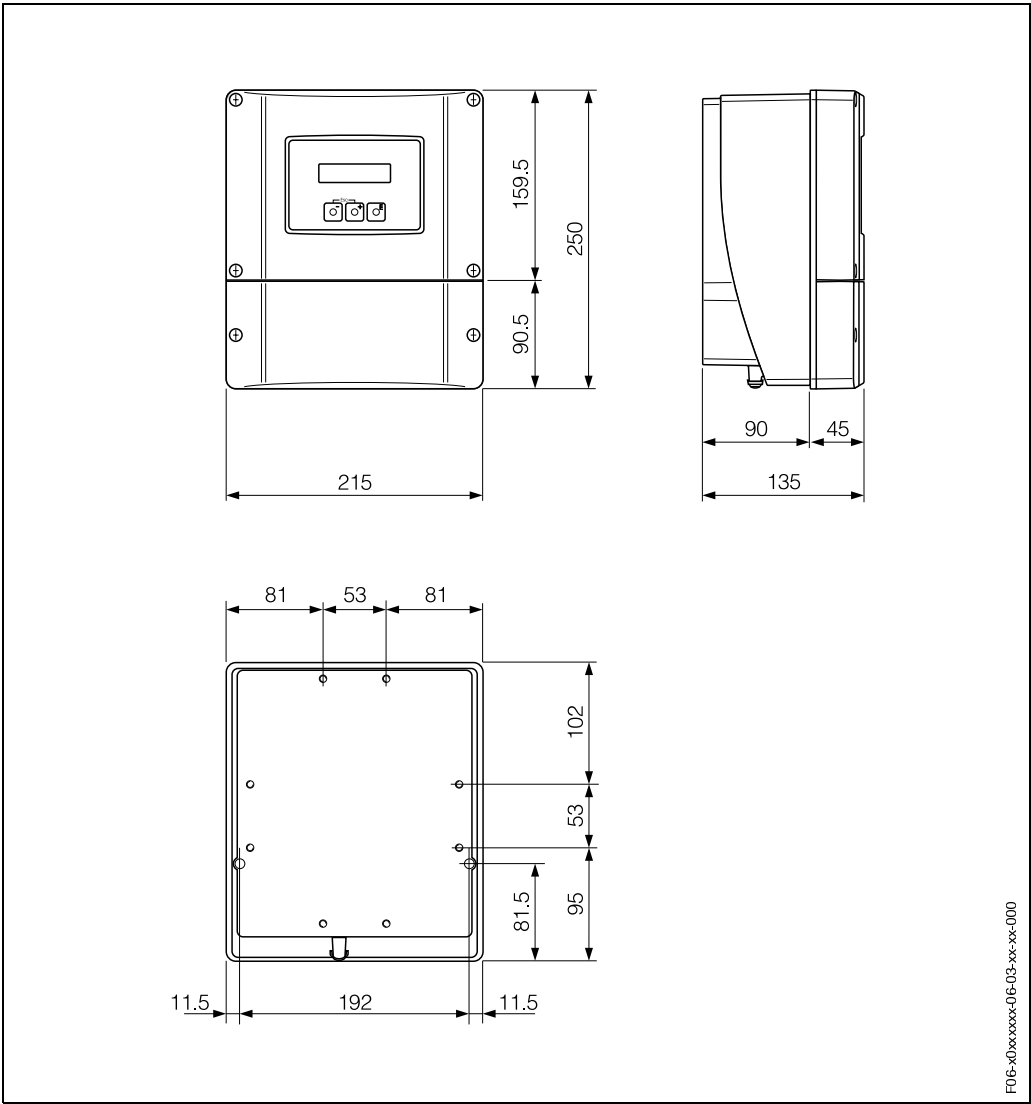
Dimensiones de la caja para montaje pared (para la instalación con panel y el montaje adosado a la tubería → página 42)
